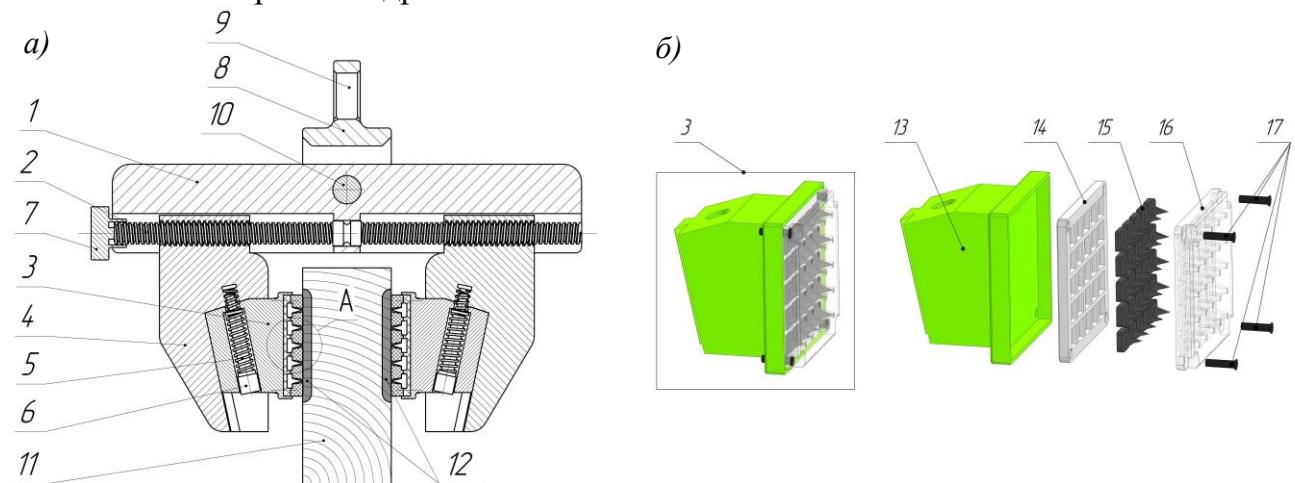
Фрикционно-зажимное ГЗУ с клиновыми ошипованными КЭ для перемещения изделий из древесины: а – общий вид; б – 3D-модель клинового ошипованного КЭ; 1 – корпус; 2 – зажимной винт; 3 – клиновый КЭ; 4 – ползун; 5 – возвратная пружина; 6 – крепежный винт; 7 – маховичок; 8 – скоба; 9 – проушина; 10 – ось; 11 – перемещаемое изделие из древесины; 12 – зона контактной поверхности; 13 – опорный корпус; 14 – упруго-эластичное основание; 15 – набор ошипованных модулей; 16 – объемно-эластичная прокладка; 17 – крепежные винты.
